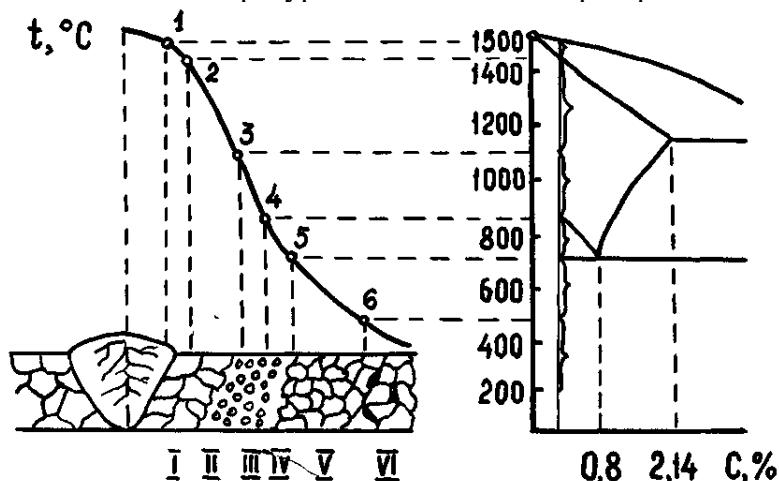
Схема структуры сварного шва:
